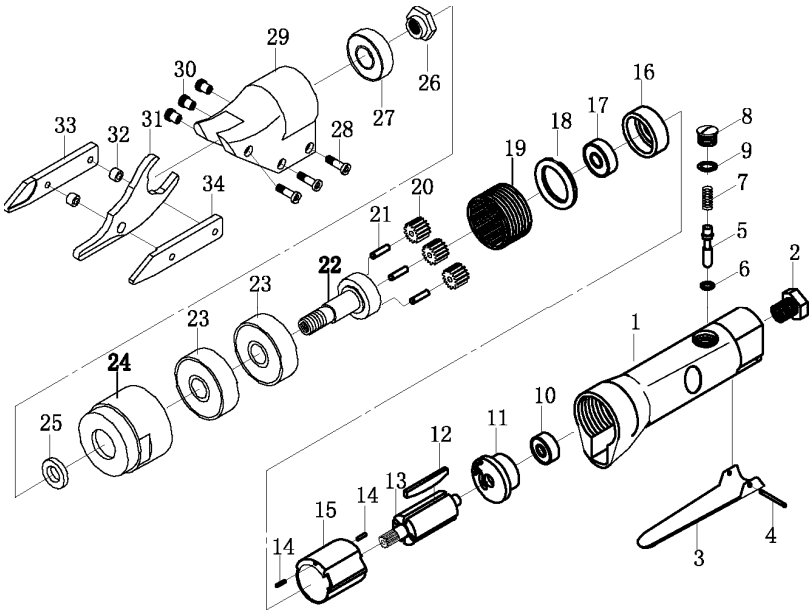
Схема устройства и сборки ножницы ручной пневматической MFX 150/006-1
